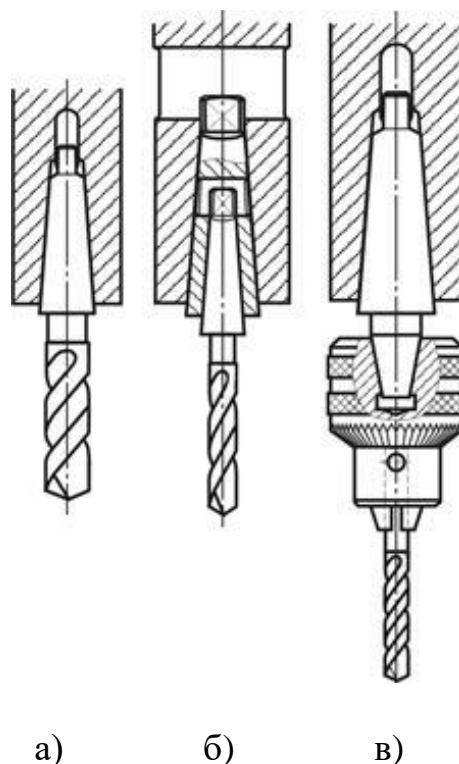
Способы крепления инструментов на сверлильных станках
